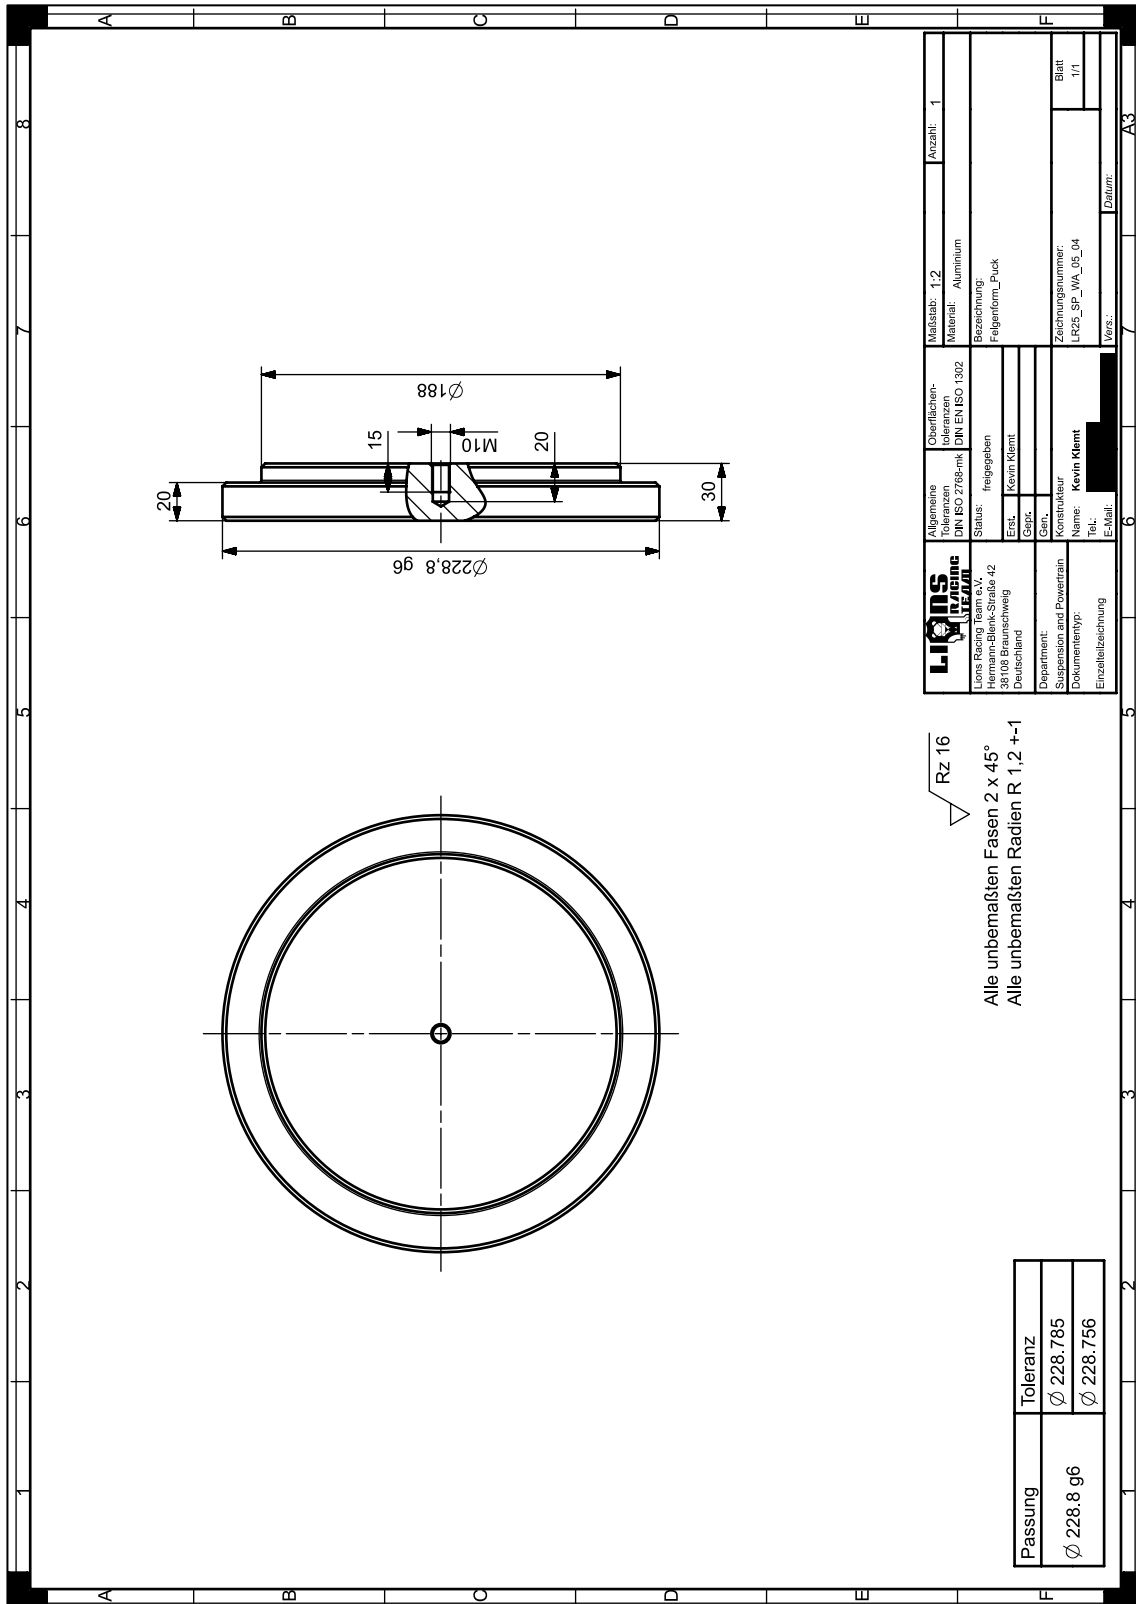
Technische Zeichnung Felgenform (4/4); Hilfsteil [42]
